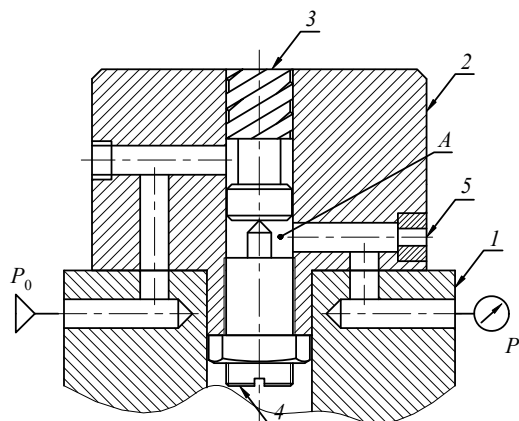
Многофункциональный пневматический вихревой элемент: 1 – корпус приспособления; 2 – штыревая опора; 3 – шнековый завихритель; 4 – установочный винт; 5 – дроссель
